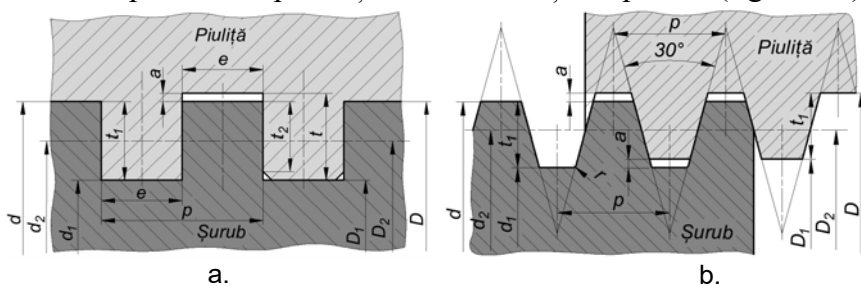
Filetul de secțiune pătrată a și trapezoidală b.
